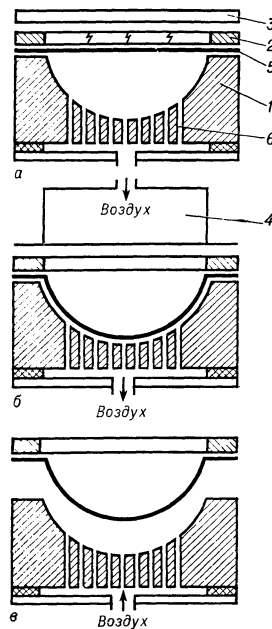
Схема негативного формования: а — нагрев; б — формование (вытяжка); в — выталкивание; 1 — матрица; 2 — зажимная рама; 3 — нагреватель; 4 — пневмокамера; 5 — заготовка; 6 — каналы для воздуха.
